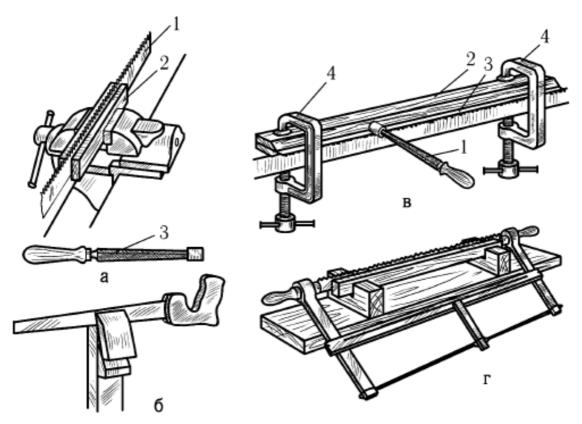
Специальные приспособления для удержания пил при заточке: a — тиски: I — пила; 2 — прокладка; 3 — напильник с резиновым наконечником для заточки;  $\delta$  — клиновой зажим;  $\delta$  — зажим струбцинами: I — напильник; 2 — прокладка; 3 — пила; 4 — струбцины;  $\epsilon$  — зажим для лучковой пилы
